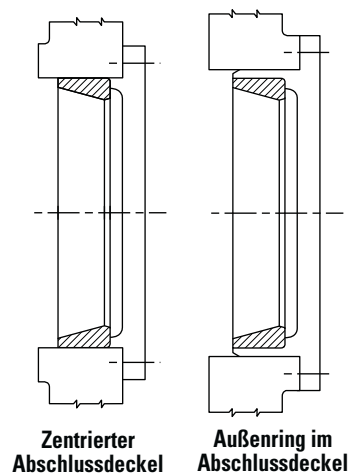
Vorrichtungen zur Lagereinstellung - direkte Montage.
